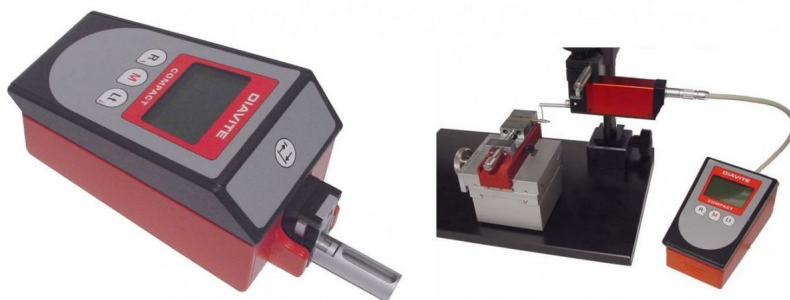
Общий вид прибора DIAVITE COMPACT
